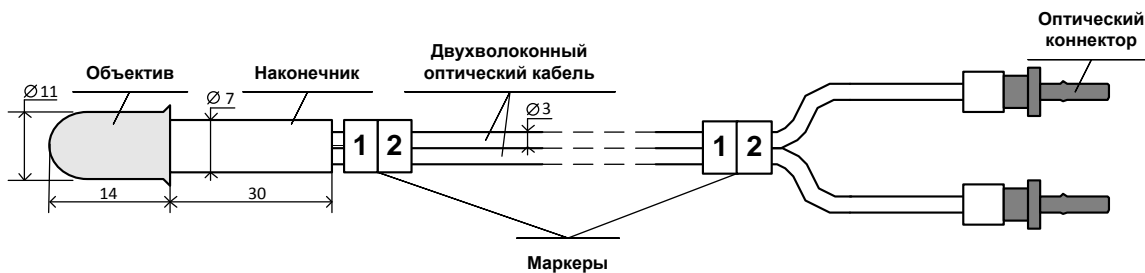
Внешний вид и габаритные размеры объектива ВОД
